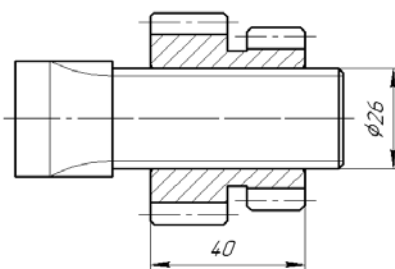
Соединение блока шестерен с валом токарного станка
